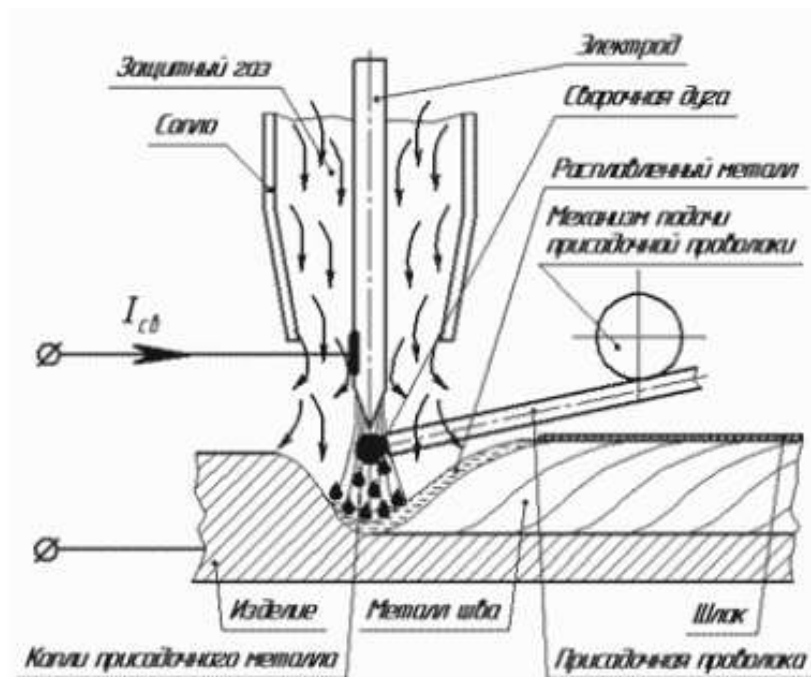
Схема сварки неплавящимся электродом с присадкой
